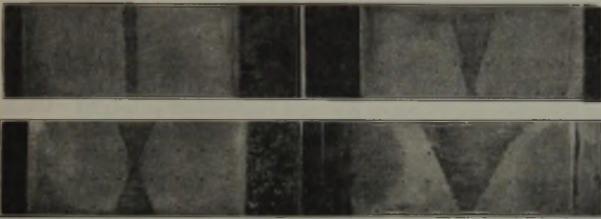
Querschliffe durch verschiedene Schweißnahtformen.
